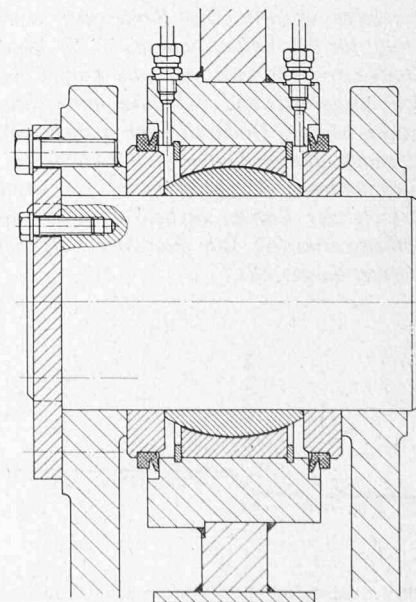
(rechts). Schwenklager des Klappen-Plungerzylinders
